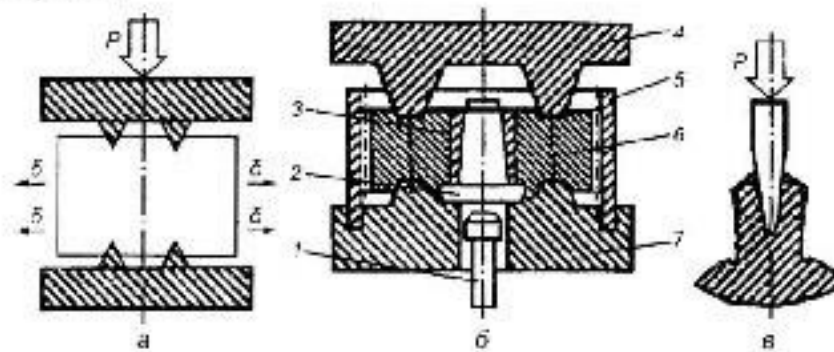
Пластическое деформирование выдавливанием: а — принципиальная схема выдавливания; б — схема выдавливания в штамп; в — схема восстановления шлица; 1 — выталкиватель; 2 — оправка; 3 — центрирующая втулка; 4 — пуансон; 5 — кольцо; 6 — заготовка; 7 — матрица
